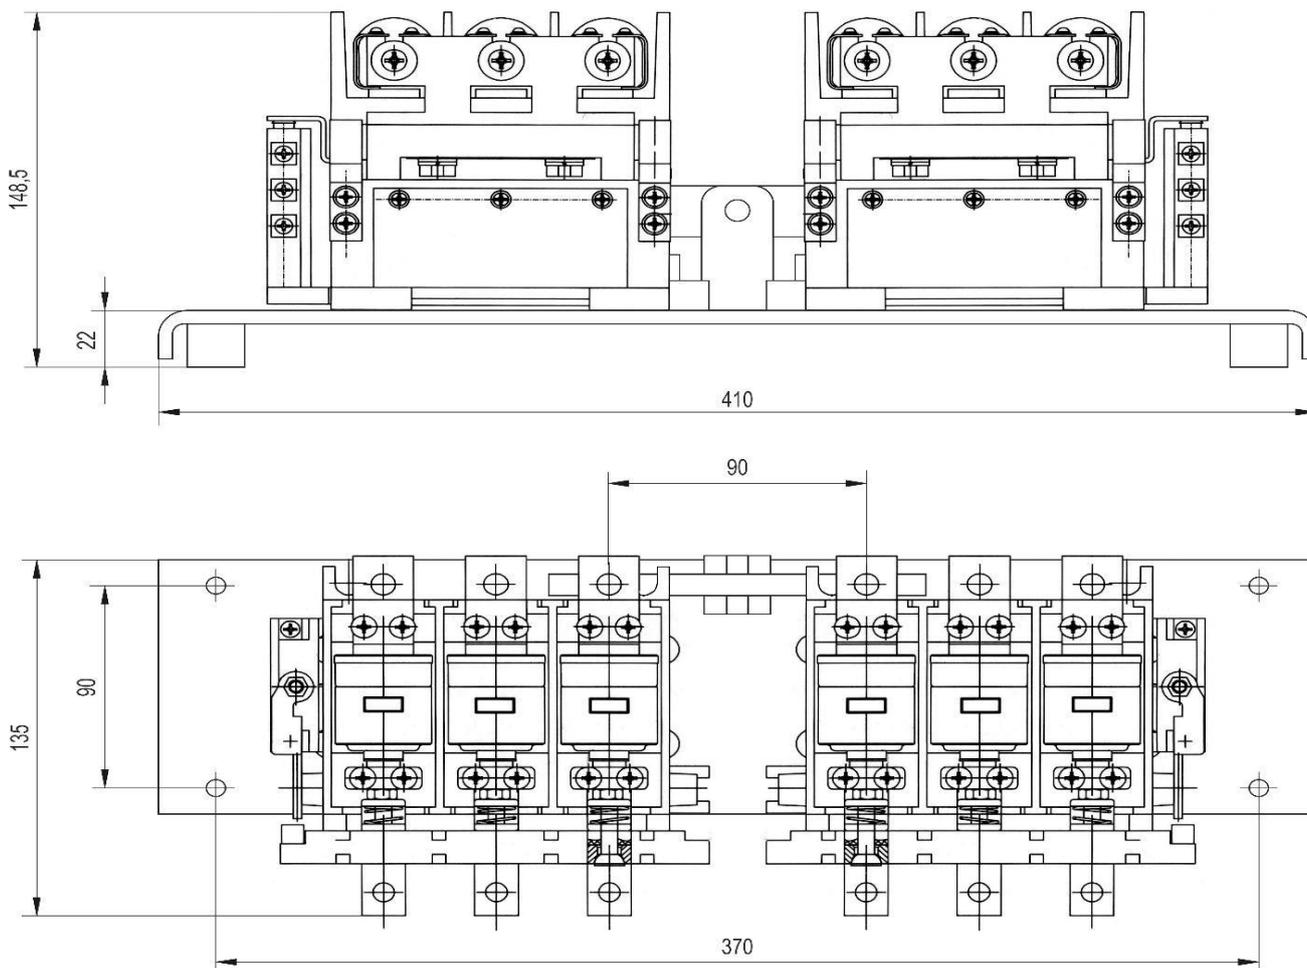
Габаритные размеры КВТ(Р)-1,14-80/125/160.
